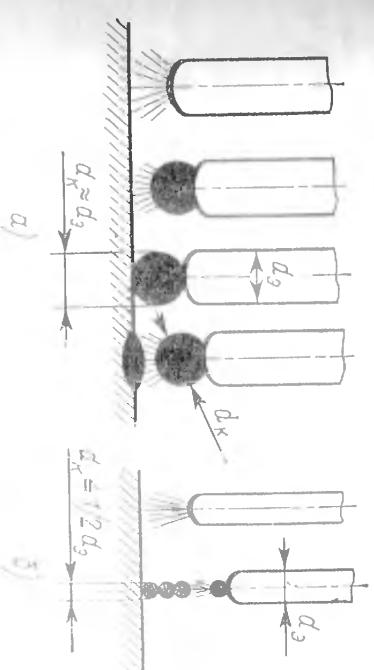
Схемы крупнокапельного (а) и струйного (б) переноса электролита на заготовку при короткой дуге:
